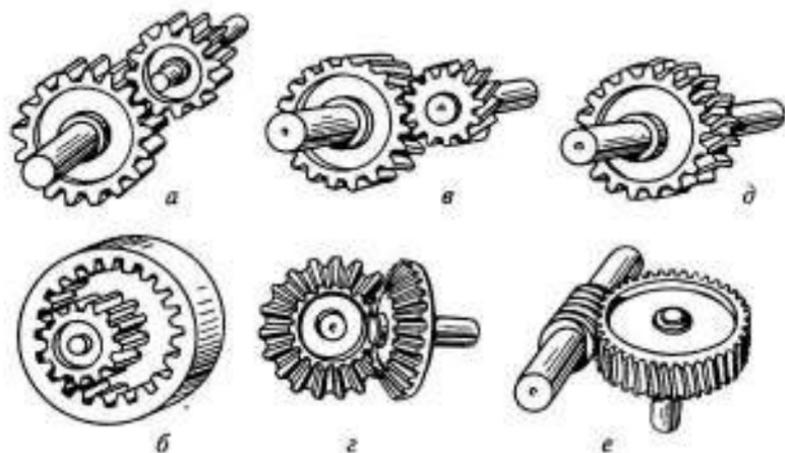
Типы зубчатых передач для вращательных движений:
